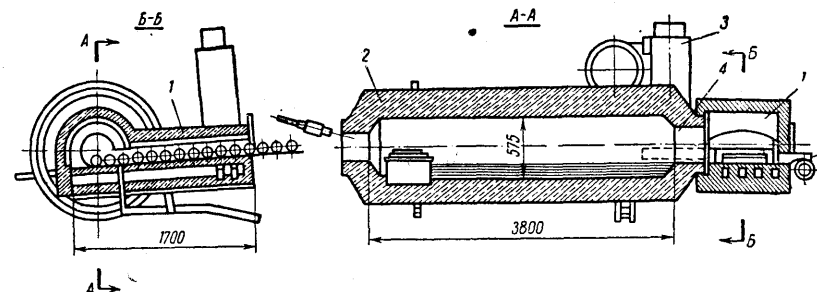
Печь для нагрева заготовок в расплавленном стекле:
